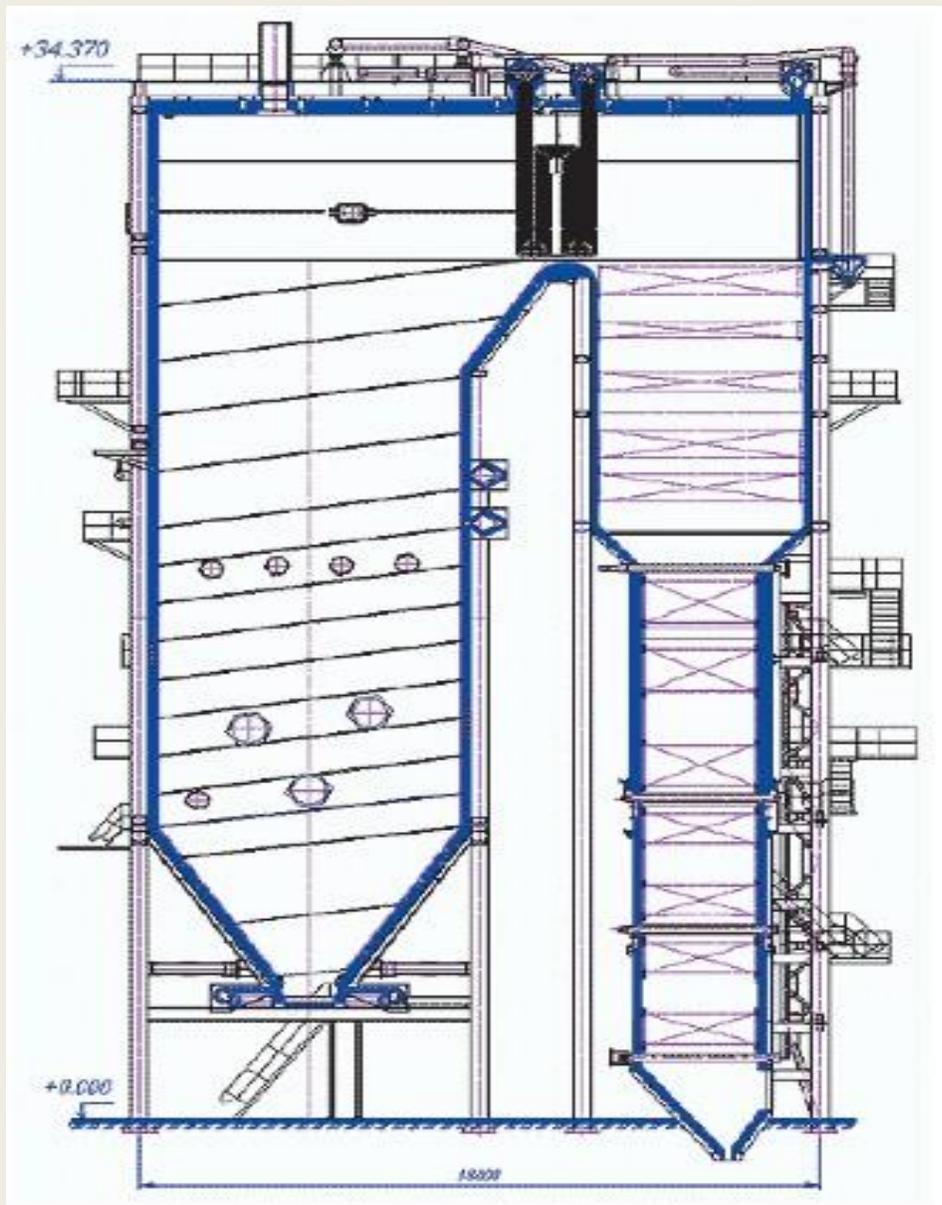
Общий вид прямоточного парового котла ПК-38-Р в разрезе
